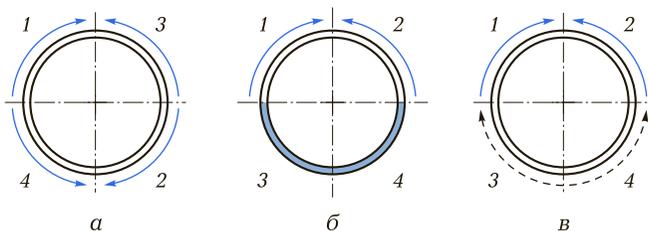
Последовательность сварки труб большого диаметра:
